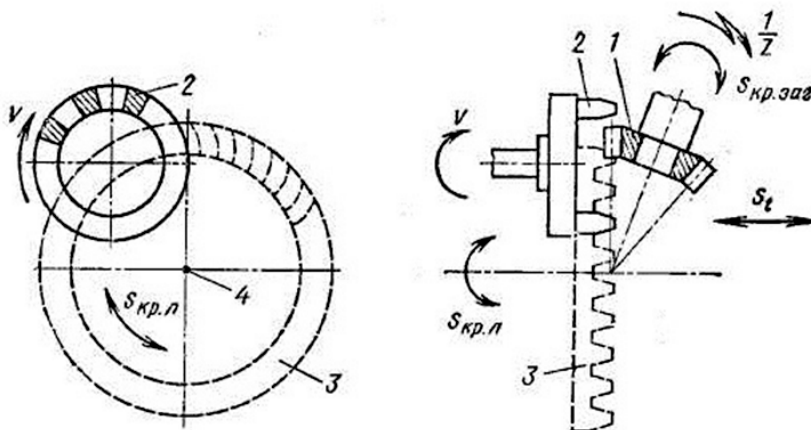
Схема нарезания конического колеса с арочными зубьями
